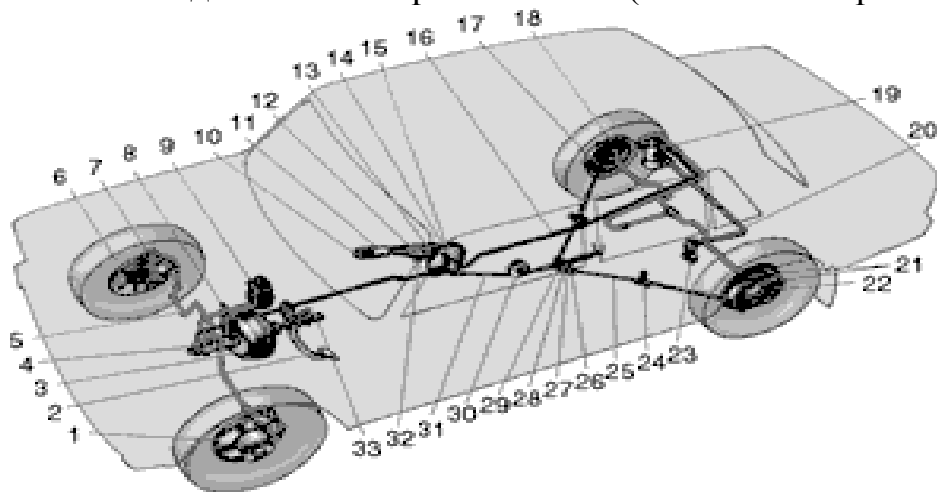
Общая схема тормозной системы 1 - передний тормоз; 2 - педаль тормоза; 3 - вакуумный усилитель; 4 - главный цилиндр гидропривода тормозов; 5 - трубопровод контура привода передних тормозов; 6 - защитный кожух переднего тормоза; 7 - суппорт переднего тормоза; 8 - вакуумный трубопровод; 9 - бачок главного цилиндра; 10 - кнопка рычага привода стояночного тормоза; 11 - рычаг привода стояночного тормоза; 12 - тяга защелки рычага; 13 - защелка рычага; 14 - кронштейн рычага привода стояночного тормоза; 15 - возвратный рычаг; 16 - трубопровод контура привода задних тормозов; 17 - фланец наконечника
